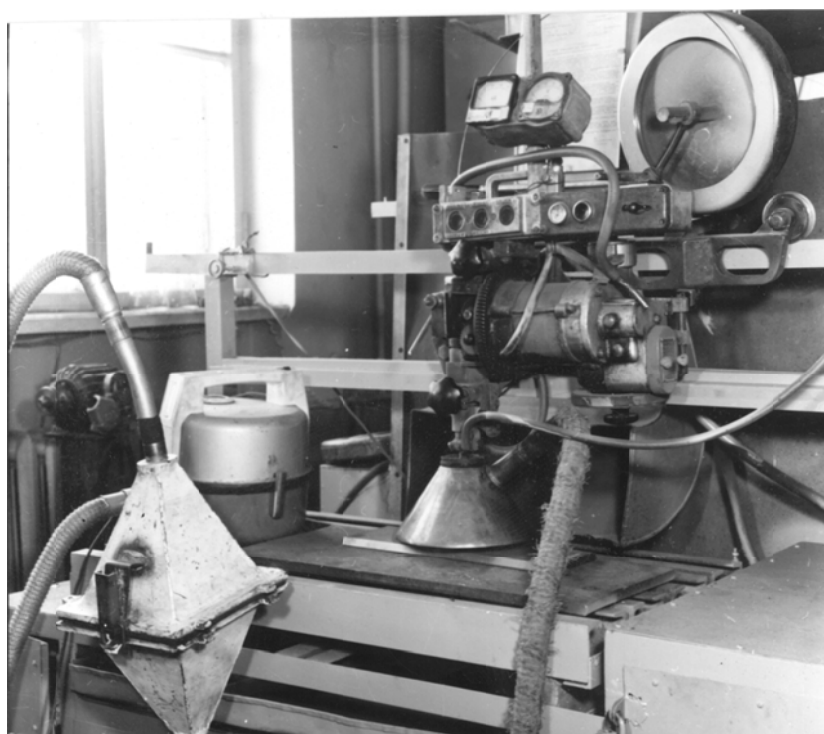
Стенд для отбора проб СА при автоматической сварке в защитных газах
